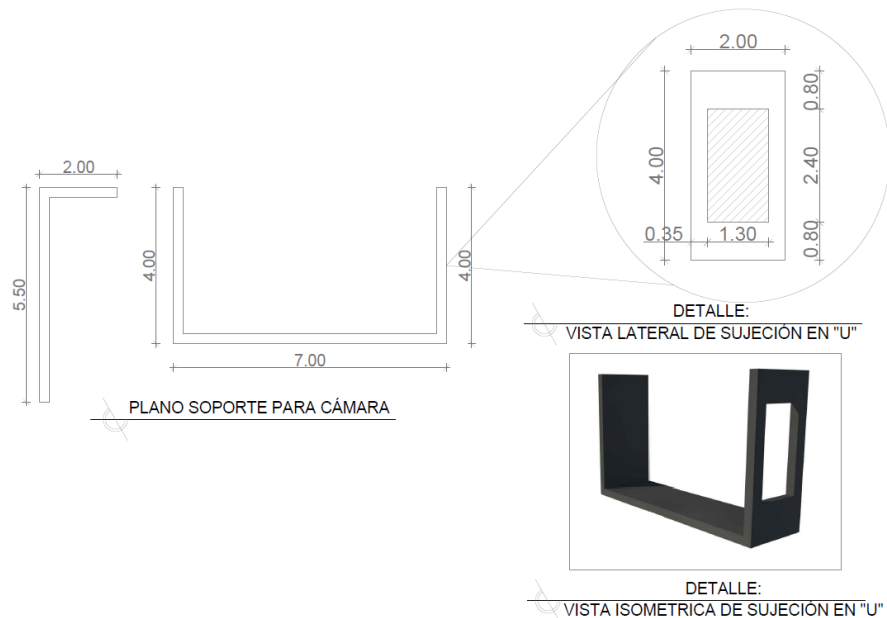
Plano de piezas para sujeción cámara. Vista frontal y lateral de piezas para sujeción de cámara a la estructura.
